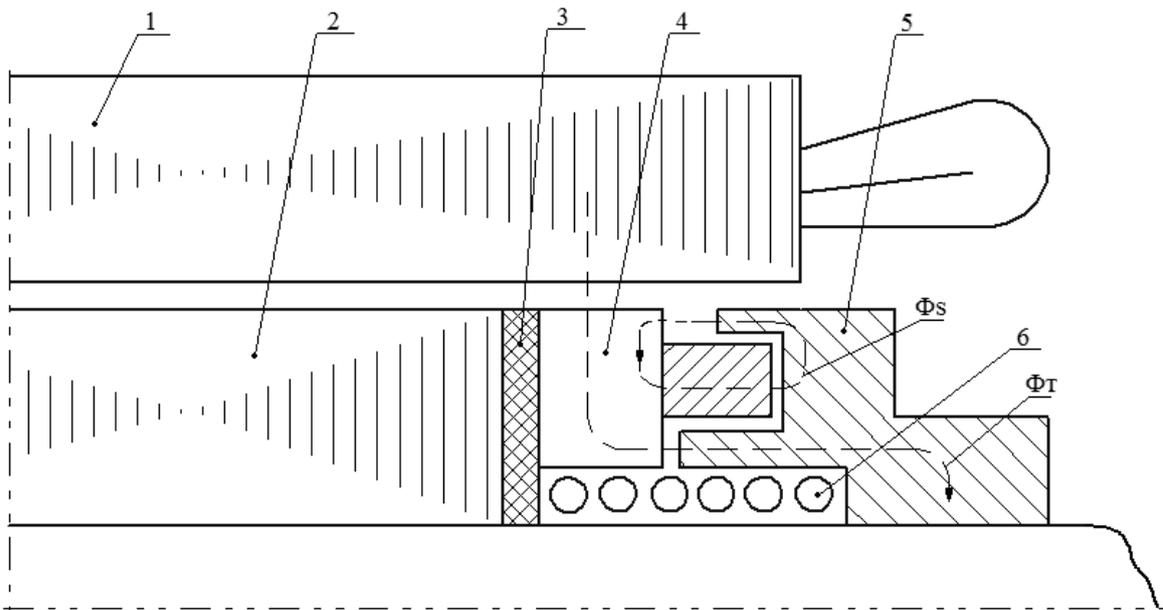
Магнитная система СЭД с электромагнитной вставкой на роторе: 1 – статор СЭД, 2 – основная часть ротора СЭД, 3 – немагнитная прокладка, 4 – тормозная часть ротора, 5 – электромагнитная вставка из магнитопроводящего материала, 6 – возвратная пружина, обеспечивающая замыкание тормоза и создание тормозного момента
